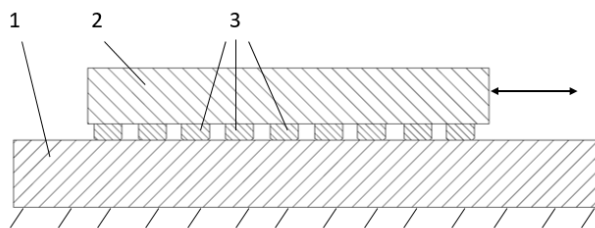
Схема пары трения прессы: 1 – неподвижная направляющая, 2 – подвижный ползун, 3 – цилиндрические элементы.
